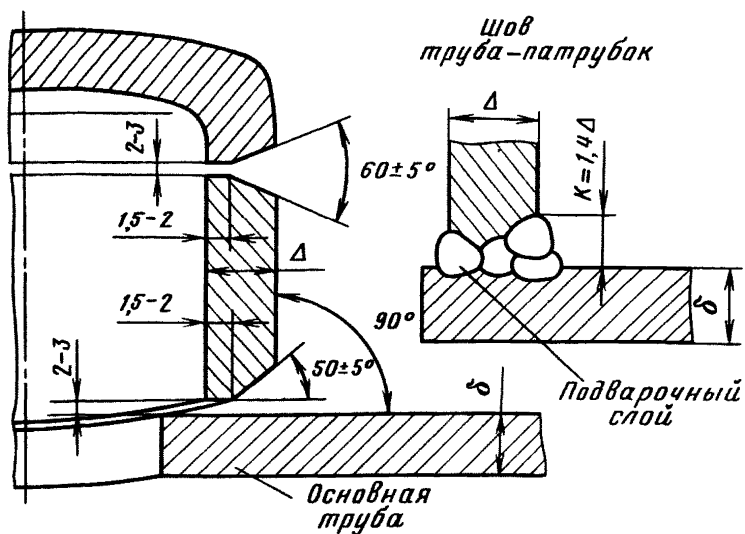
Схема подготовки трубы и патрубка под сварку при заделке технологических отверстий с помощью патрубков
